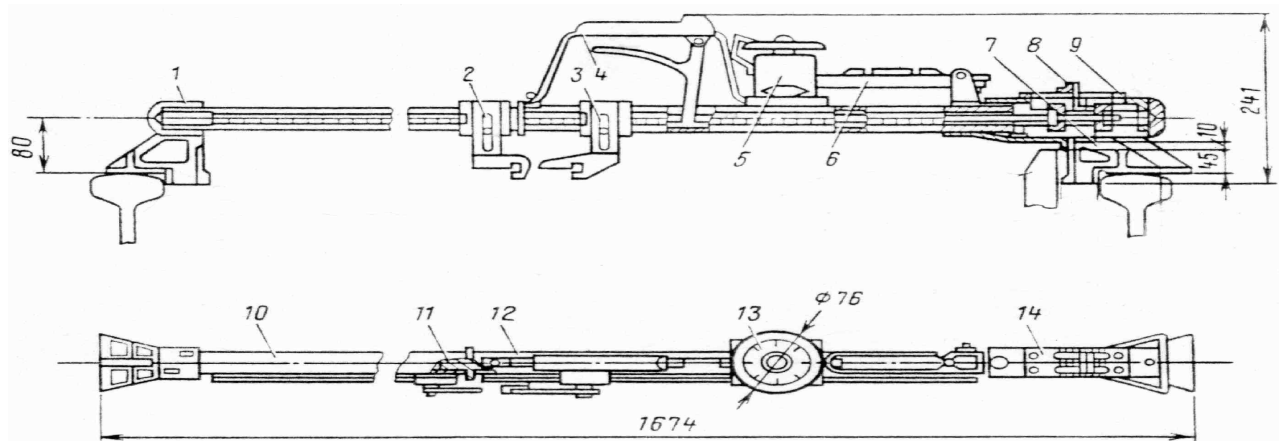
Контрольний шаблон типу ЦУП – 3Д: 1 – нерухомий упор; 2,3 – шаблони ординат; 4 – ручка; 5 – корпус рівня; 6 – рівень; 7 – рухомий упор; 8 – показник ширини колії; 9 – напрямна; 10 – корпус шаблону; 11 – ізоляційна бобишка; 12 – права частина корпусу; 13 – шкала рівня; 14 – шкала шаблону
